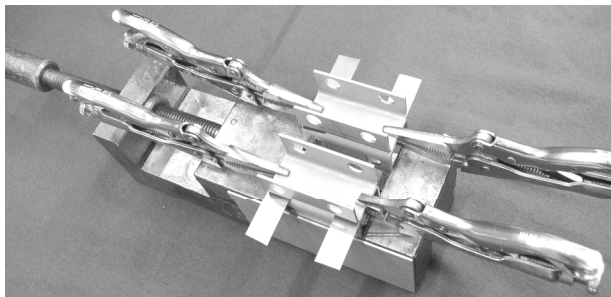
Fixierung und Ausrichtung der KS2-Probenkörper während des Schweißvorgangs.
